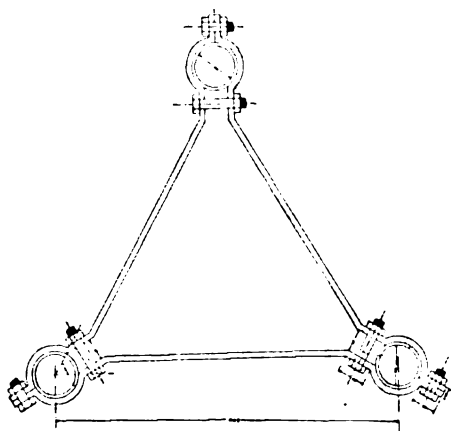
Dettaglio della briglia. torre della centrale, suo piano contenente, nel superiore, i parafulmini Siemens e sca-
